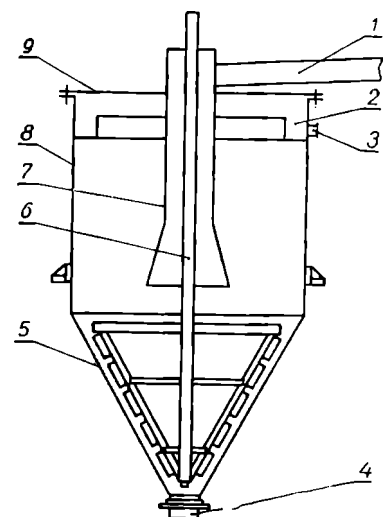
Отстойник типа Брандес: 1, 7 — труба для раствора; 2 — кольцевой желоб; 3 — штуцер для слива; 4 — штуцер для отвода шлама; 5 — днище; 6 — мешалка; 8 — цилиндрический корпус; 9 — крышка.
